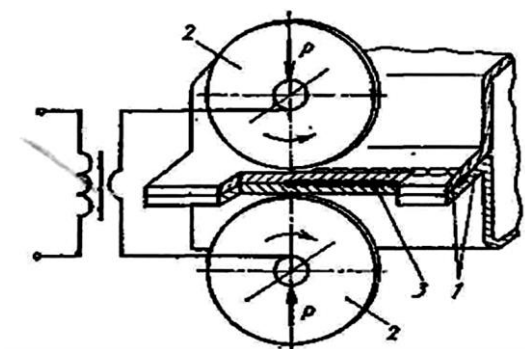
Схема шовной сварки: 1- заготовка, 2- сварочные электроды
